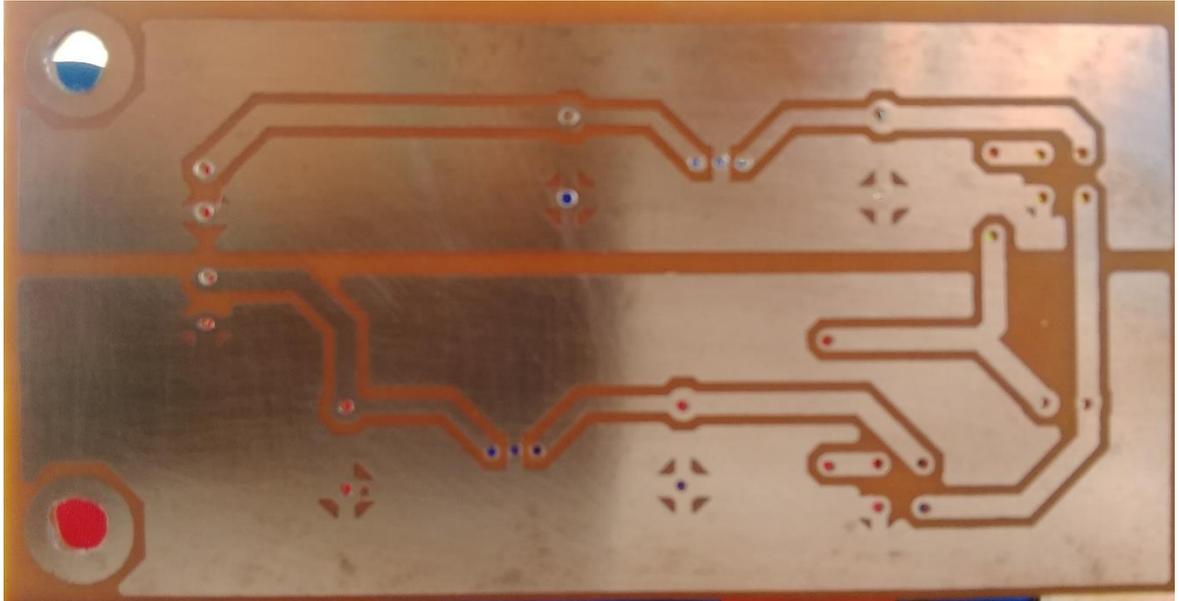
Revelado de PCB fuente de alimentación etapa de acondicionamiento
